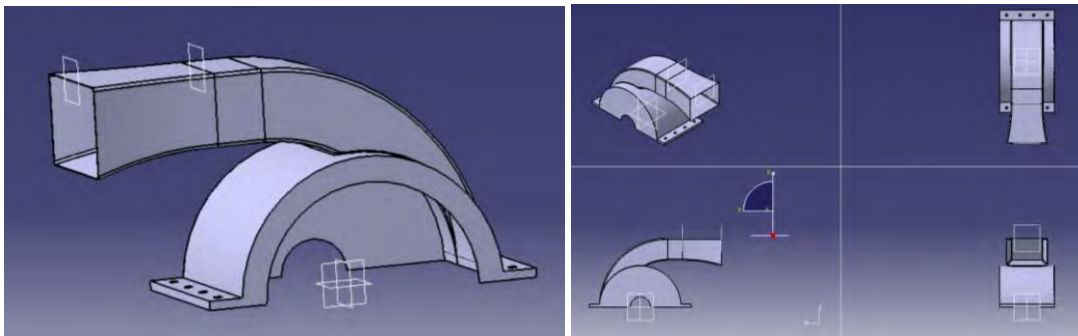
Vistas del dibujo mecánico del aditamento para el ducto de aire del soplador (realizado en Catia V5)
